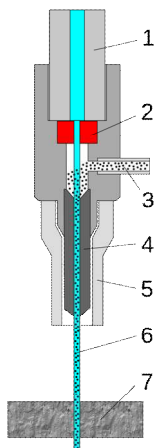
Схема установки гидроабразивной резки: 1 – подвод воды под высоким давлением; 2 – сопло; 3 – подача абразива; 4 – смеситель; 5 – кожух; 6 – режущая струя; 7 – разрезаемый материал
